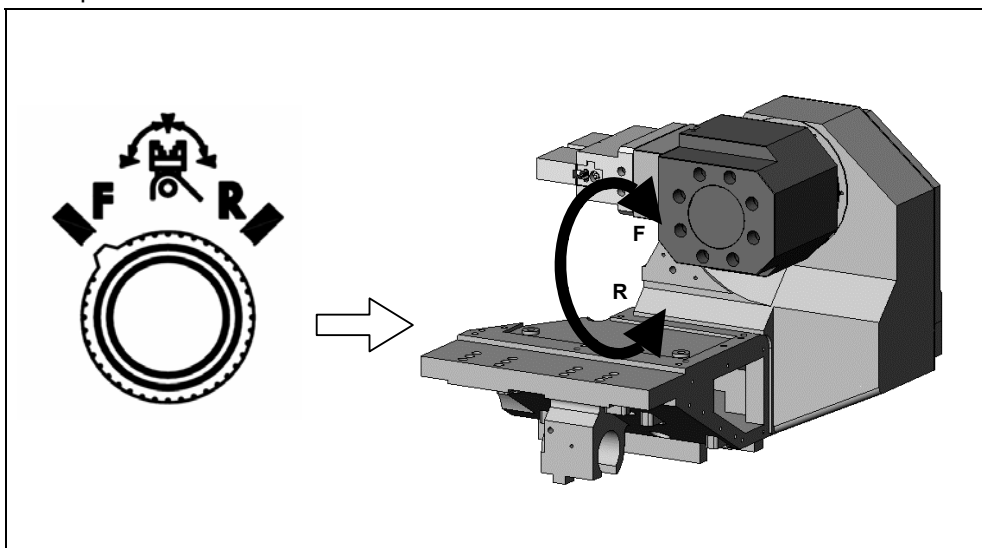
Поворот зажимного приспособления при помощи переключателя направления индексирования устройства загрузки-разгрузки заготовки.
